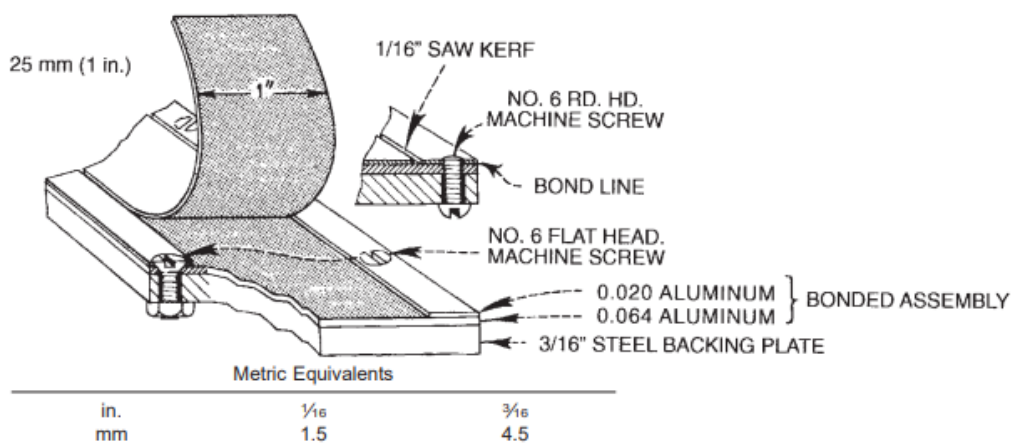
Dimensões provetes para ensaio *climbing drum* [50]
